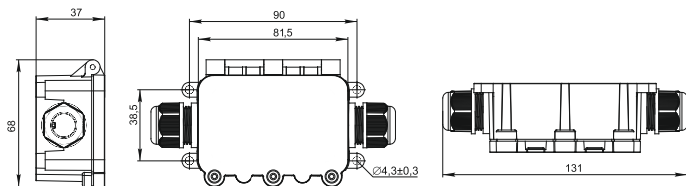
Габаритные размеры коробки WTP-406 / Figure 6 – Overall dimensions of the WTP-406 box
